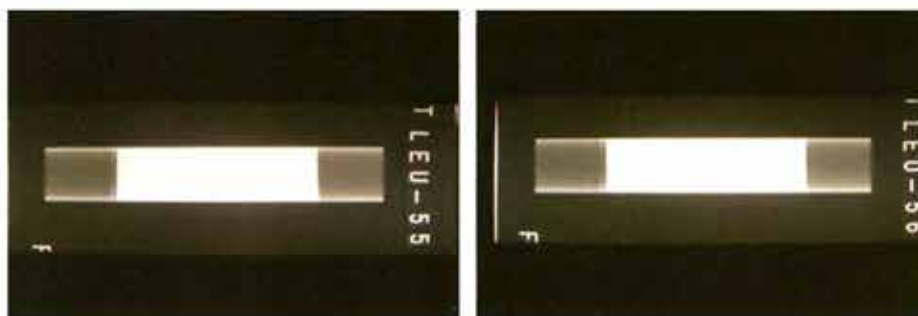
Cordón de soldadura del blanco anular desgasificado.
